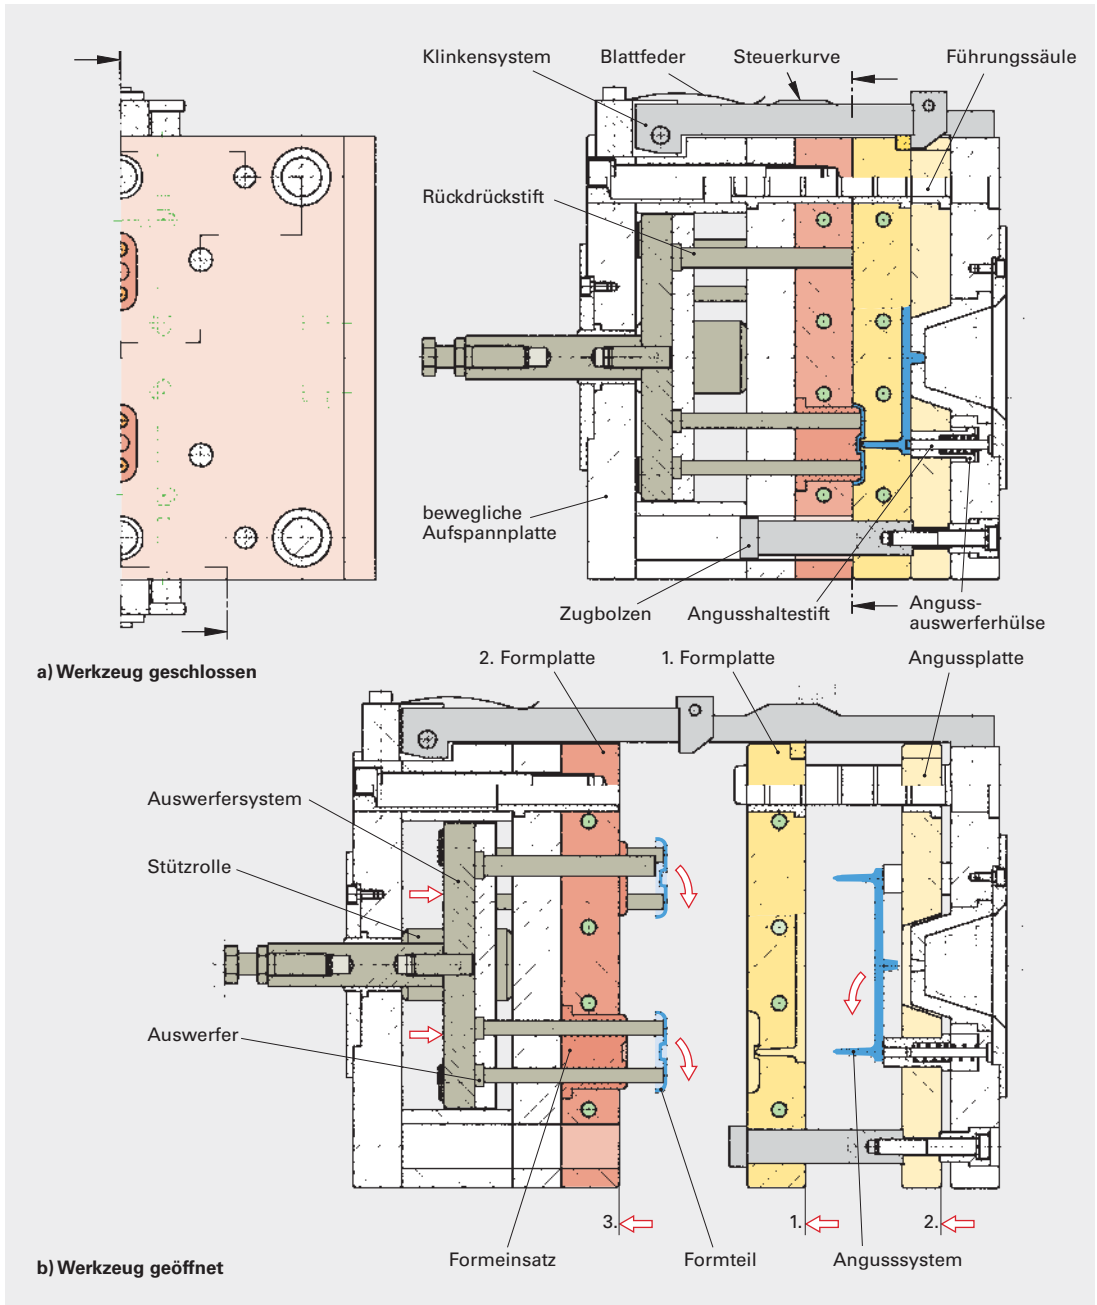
Dreiplattenwerkzeug für Abschlussdeckel
